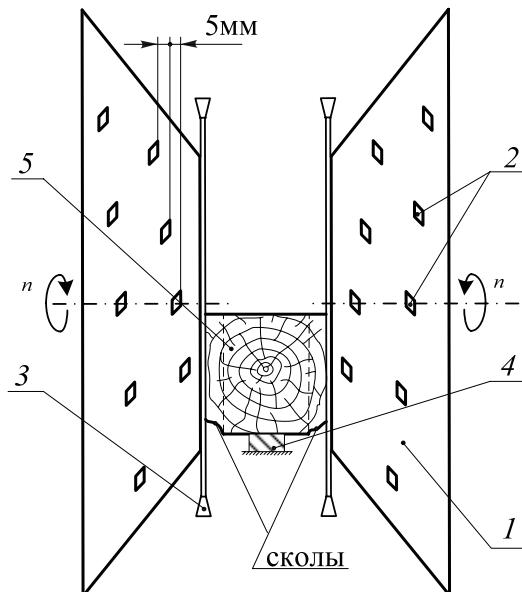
Схема обработки древесины на фрезерно-брусующих станках:
